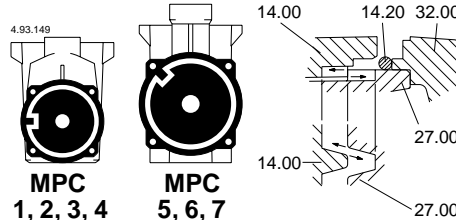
Ориентиры для сборки корпуса насоса (14.00) - крышки диффузора (27.00)
